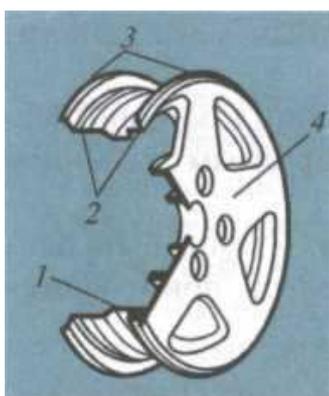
Основные элементы конструкции автомобильного колеса:
